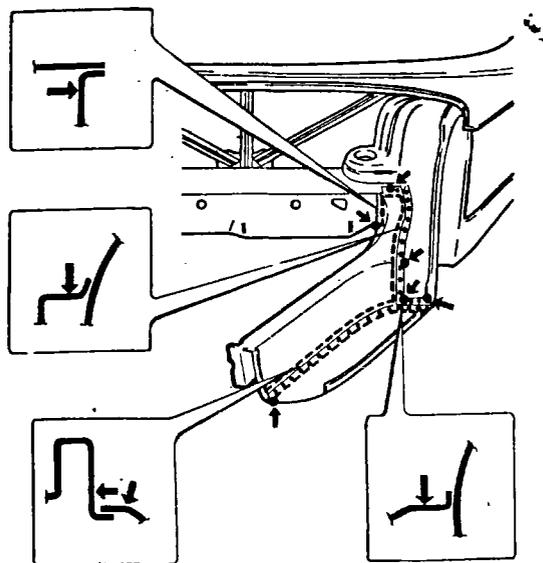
Замена пола топливного бака (запасного колеса) и лонжеронов пола задка. Пунктиром обозначены линии рубки, точками - швы контактной сварки. На основном виде стрелками показаны места газовой сварки, стрелками на фрагментах - места рубки
